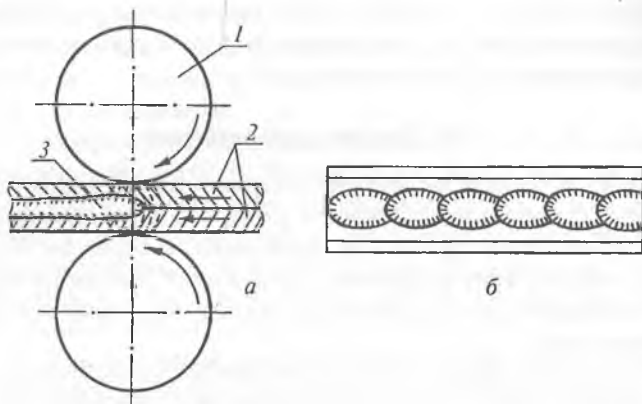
Схема роликовой сварки: а — схема образования соединения: 1 — вращающиеся медные электроды; 2 — свариваемые детали; 3 — сварной шов; б — макроскопическое строение роликового шва
